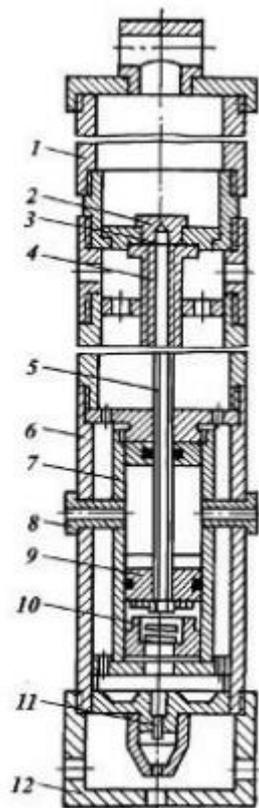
Глубинный жидкостный дозатор: 1 – верхний контейнер; 2 – штуцер перепускной; 3 – игла; 4 – патрубок; 5 – шток; 6 – нижний контейнер; 7 – цилиндр; 8 – патрубки; 9 – поршень; 10 – пружины; 11 – штуцер с дозировочным отверстием; 12 – камера.
